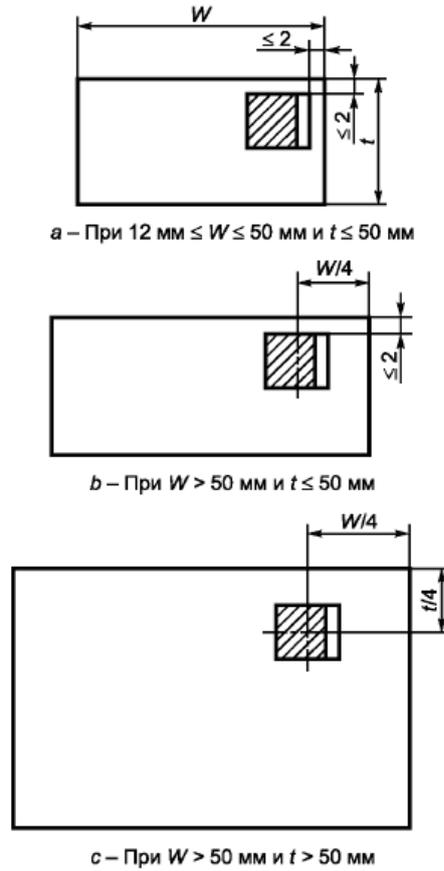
Сортовой прокат квадратного и прямоугольного сечений. Места вырезки испытательных образцов для испытаний на ударный изгиб (по ГОСТ 53845–2010)
